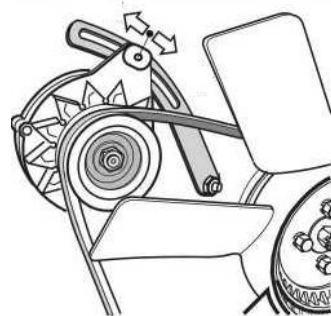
6 Inspección y ajuste de tensión de correa de ventilador
